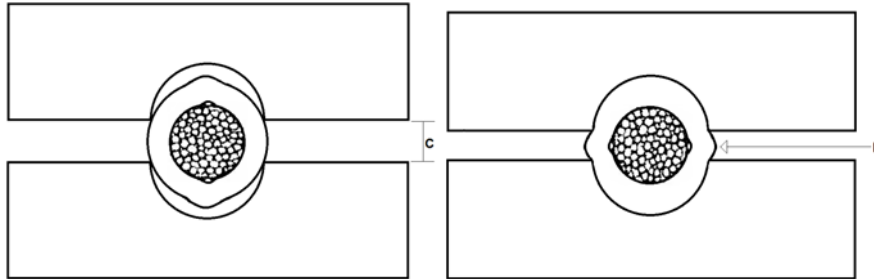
L'accessoire a tourné à 90°. Les faces de la matrice sont fermées pour un 1er contact
